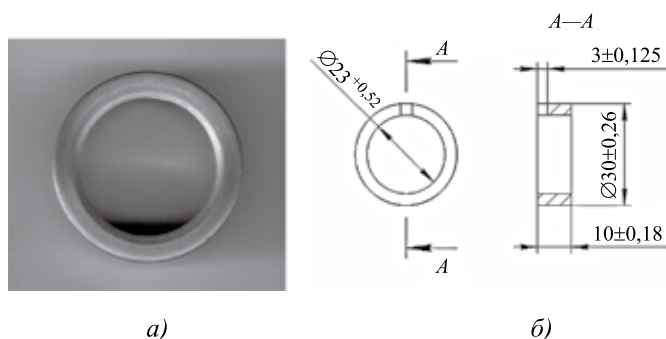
Внешний вид (а) и размеры (б) образцов для испытания на износ
